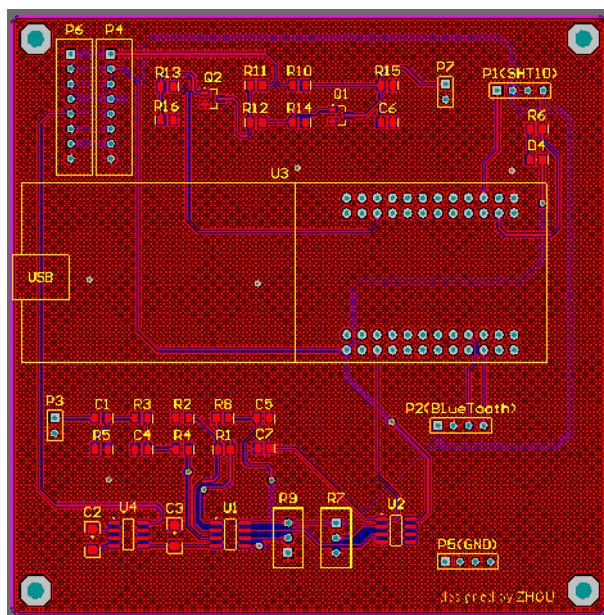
使用 Altium Designer 开发的 PCB 图（2D 视图）
